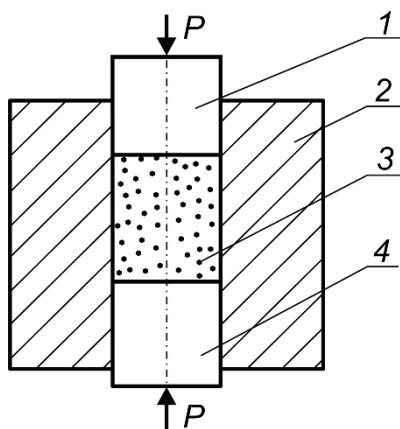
Схема прессования порошка в жесткой пресс-форме: 1 – верхний стальной пуансон, 2 – стальная матрица, 3 – порошок, 4 – нижний стальной пуансон
